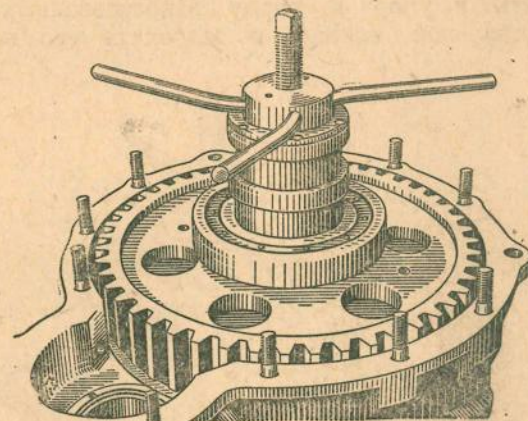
Запрессовка ведомой шестерни на хвостовик солнечной шестерни
